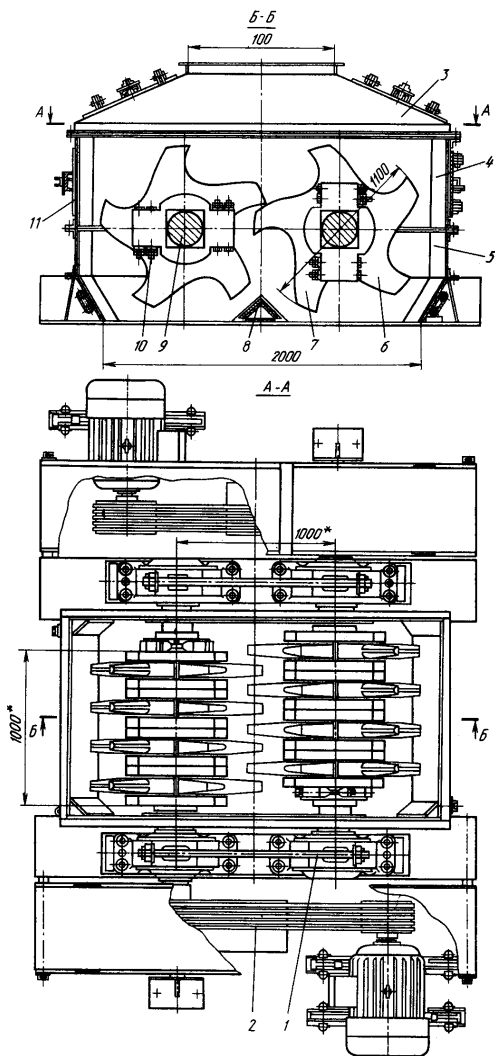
Двухвалковая зубчатая дробилка СМД-153.
